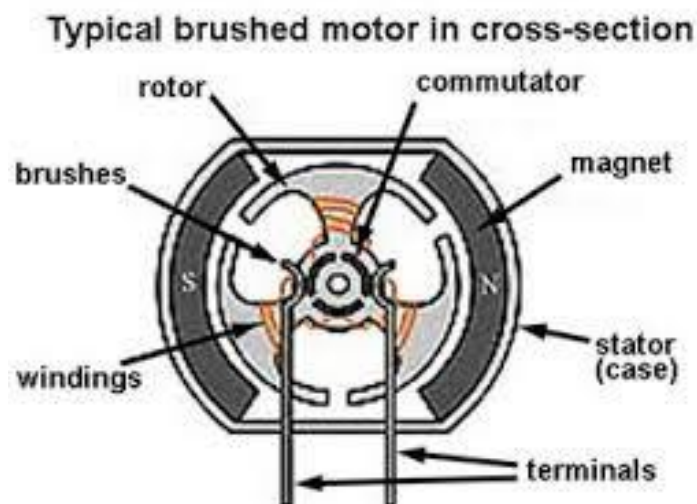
Fuente: <https://www.renesas.com/eu/en/support/technical-resources/engineer-school/brushless-dc-motor-01-overview.html>
